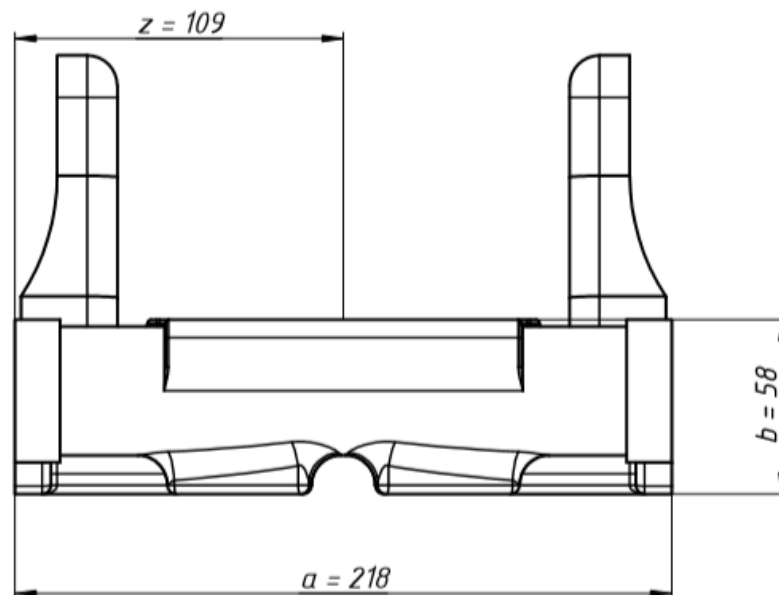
Параметри базової поверхні за її вертикального розташування
